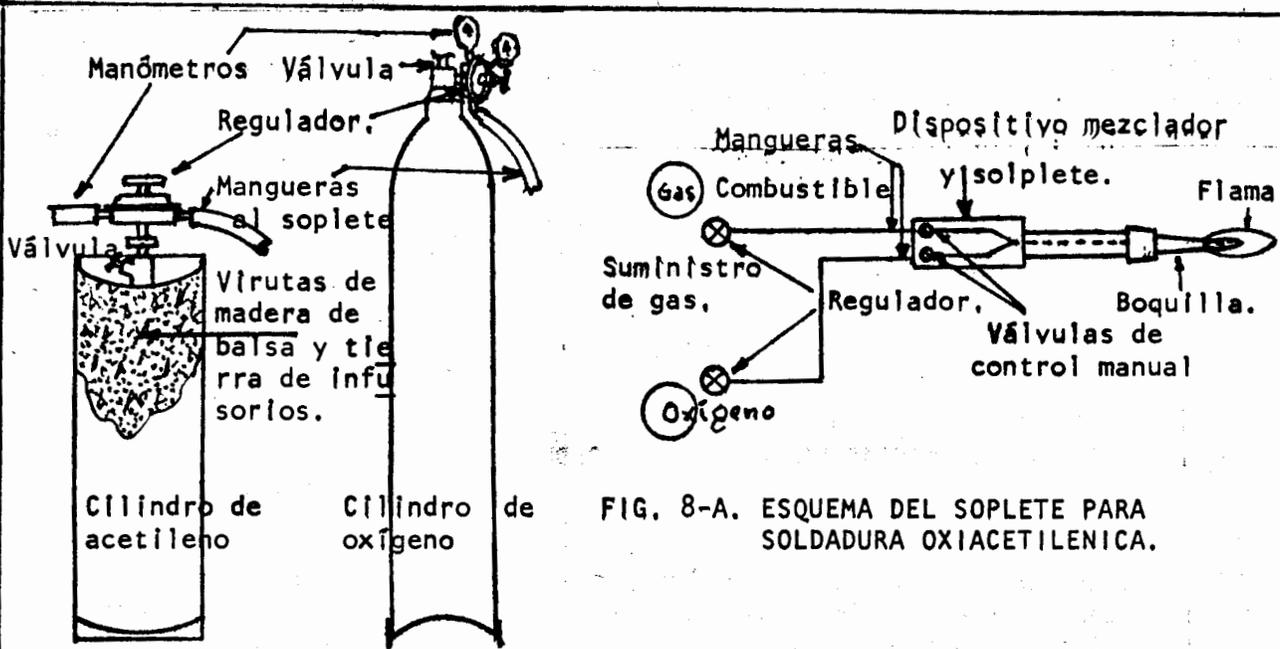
A. ESQUEMA DEL SOPLETE PARA SOLDADURA OXIACETILENICA.
